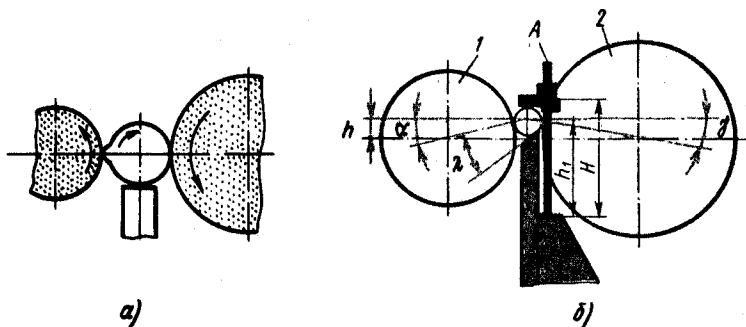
Наладка бесцентрово-шлифовального станка: а — погрешности обработки, б — установка углов с помощью устройства А; 1 — ведущий круг, 2 — шлифовальный круг
